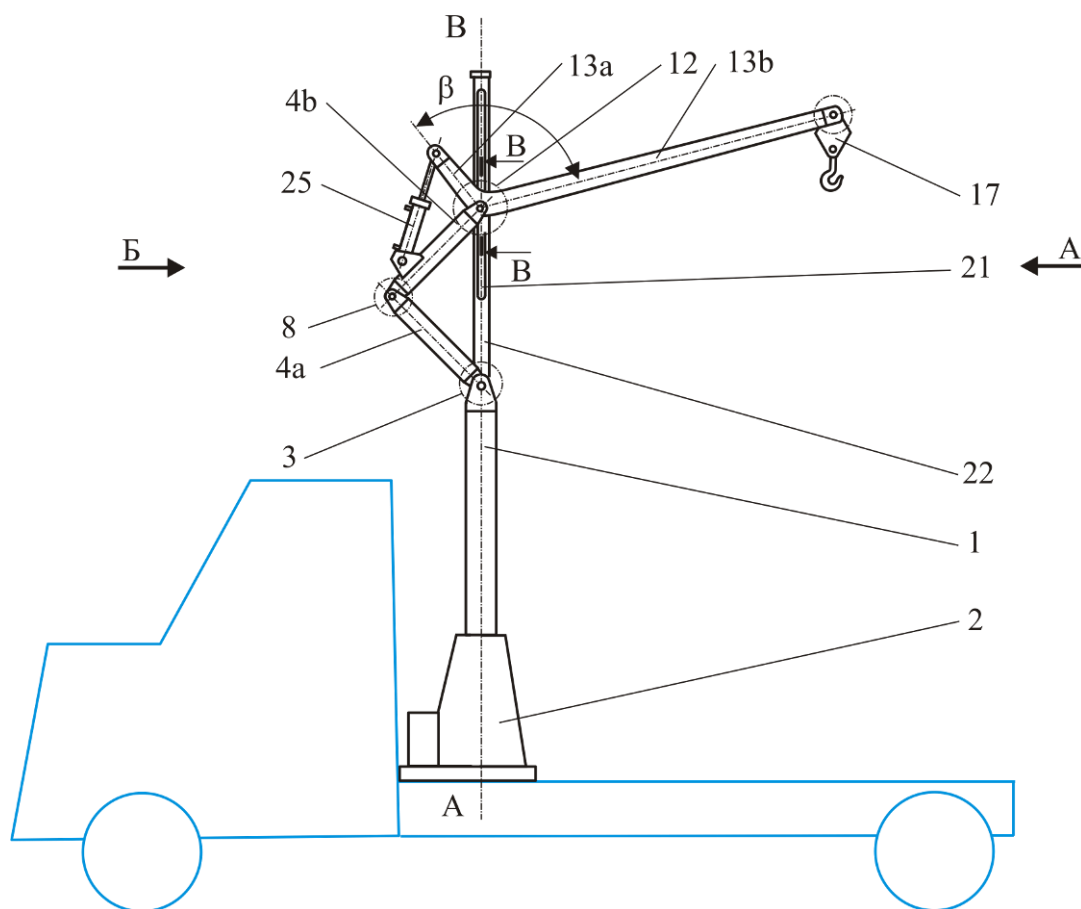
Общий вид сбоку крана-манипулятора энергоэффективной конструкции [10]: 1 - опорно-поворотная конструкция; 2 – основание; 3 - шарнирное соединение; 4 – корневая секция стрелы; 4а, 4b, 13а, 13b – звено; 5, 6, 9, 10, 14, 27 – проушина; 7, 11, 16, 28, 30 - шарнирный палец; 8, 12 - шарнирное соединение; 13 – концевая секция стрелы; 15 - боковая стенка; 17 - грузозахватный орган; 18, 25 - силовой гидроцилиндр; 19, 26, 29 – серьга; 20 - подшипниковая обойма; 21 – паз; 22 – направляющая; 23 – вырез; 24 - ребро жесткости
